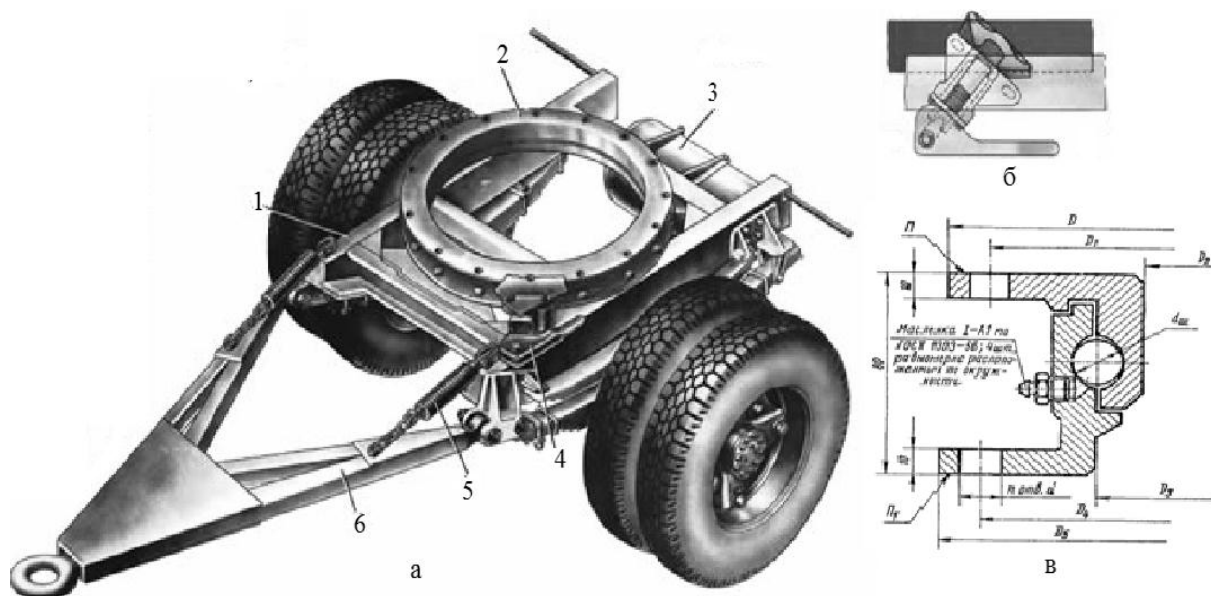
Поворотная тележка прицепа ГКБ 8350:
